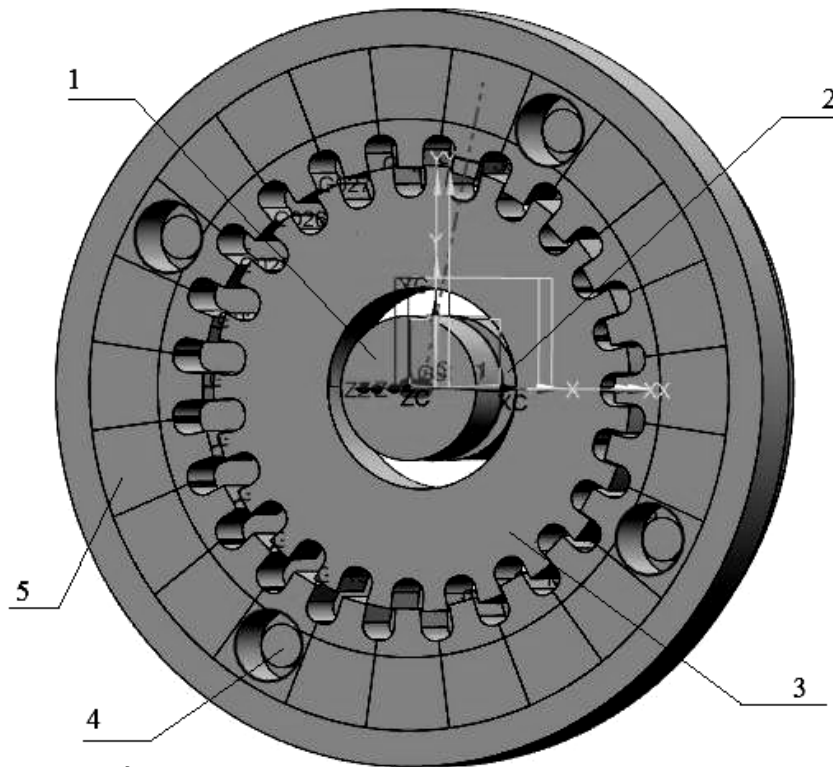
Вид компьютерной модели эксцентриковой передачи с поступательным движением сателлита: 1 – входной вал; 2 – эксцентрик входного вала; 3 – центральное зубчатое колесо; 4 – ось; 5 – сателлит
